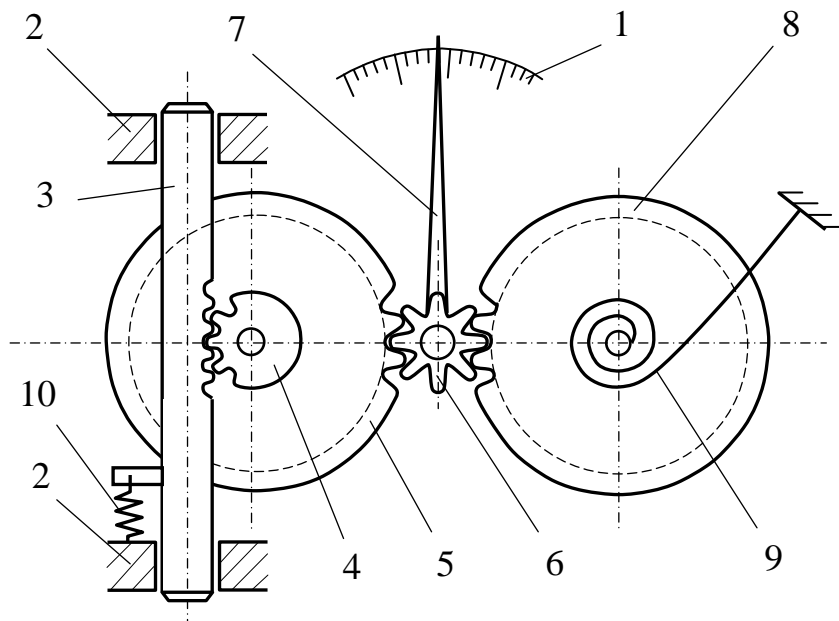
Принципиальная схема индикаторной головки: 1 – шкала; 2 – корпус; 3 – измерительный стержень; 4 – малое зубчатое колесо; 5 – большое зубчатое колесо; 6 – триб; 7 – стрелка; 8 – ведомое зубчатое колесо; 9 – пружина стрелки; 10 – пружина измерительного стержня
